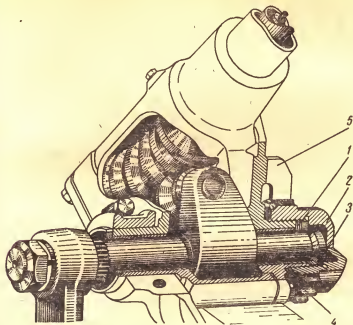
Регулировка зацепления ролика с червяком автомобиля ЗИЛ-164:
